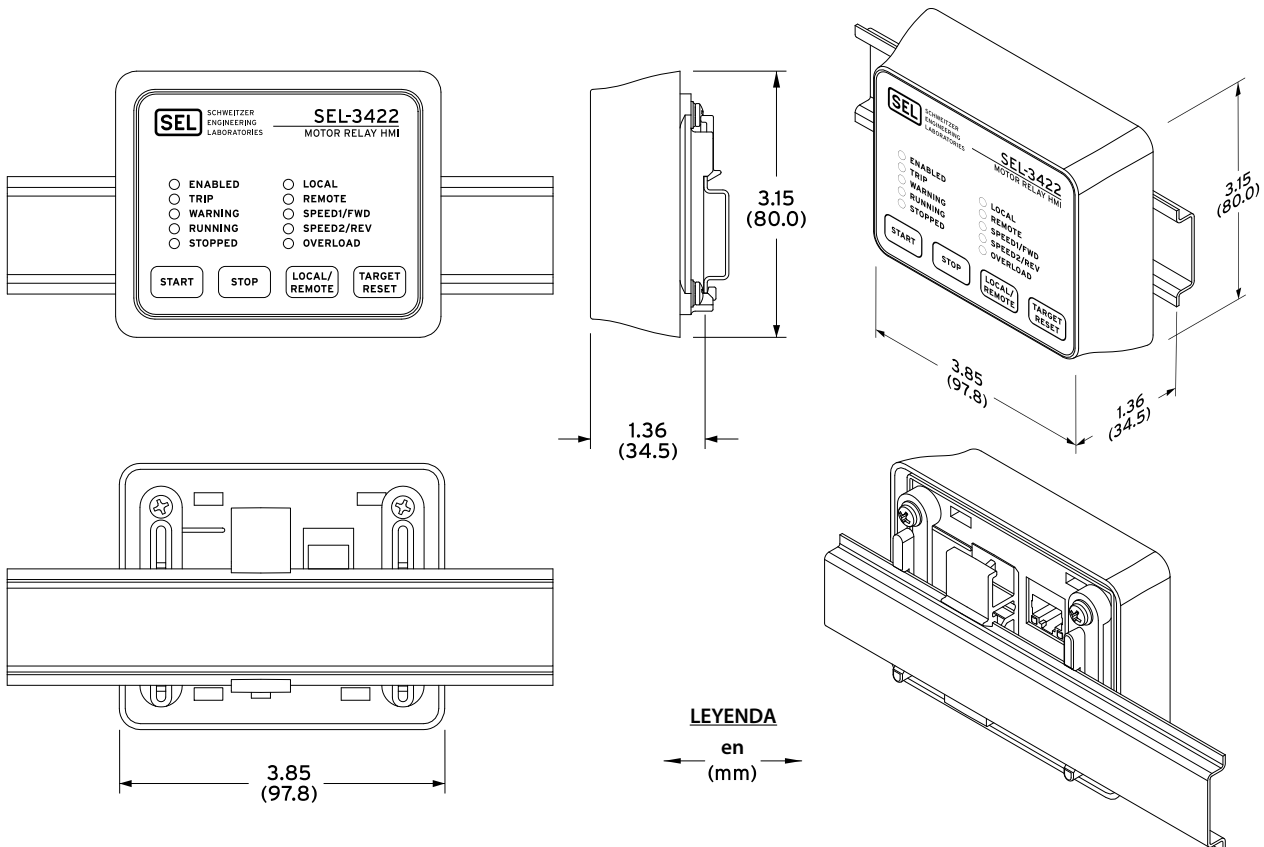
Dibujos de la Instalación de la IHM del Relé de Motor SEL-3422 (Montaje en Riel DIN)
